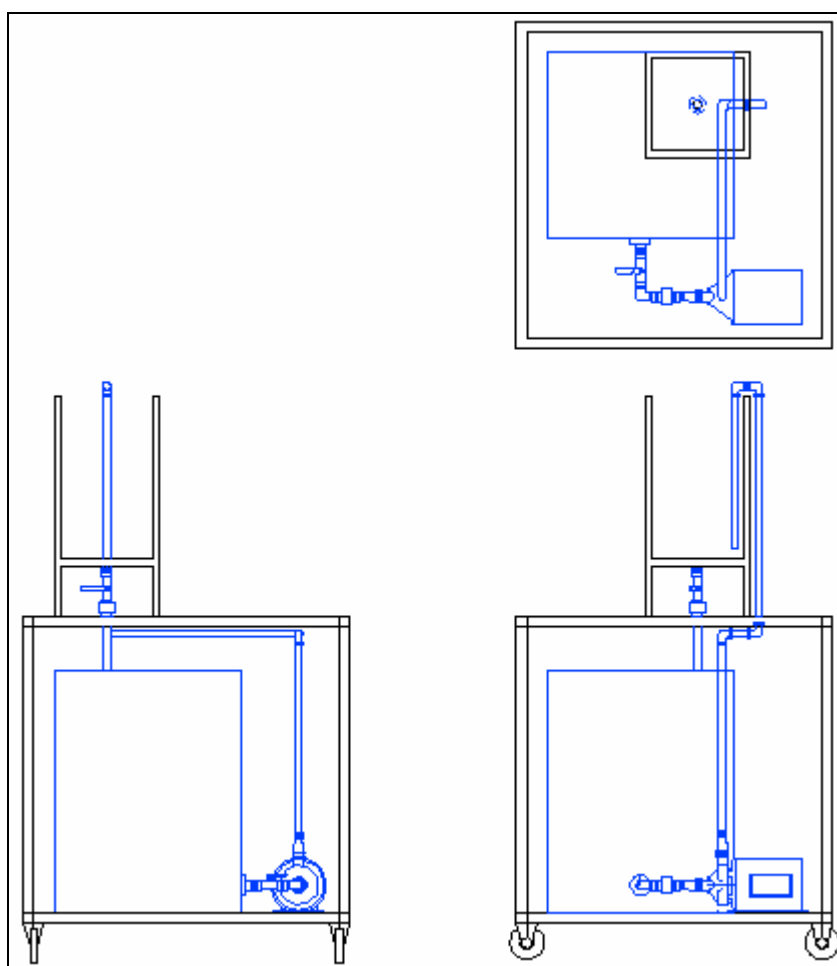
ESTRUCTURA DE PLANTA DE CONTROL DE NIVEL.
